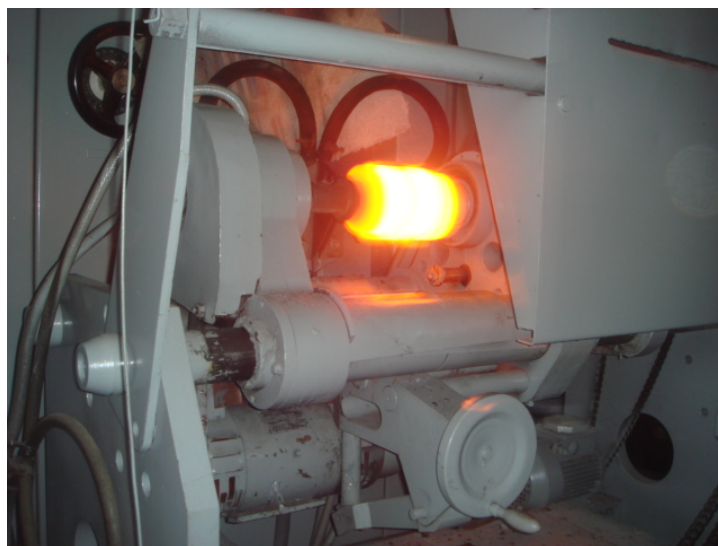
Процесс изготовления двухслойного антифрикционного изделия (биметаллической втулки подбивочного блока выправочно-подбивочно-рихтовочной машины ВПР)
